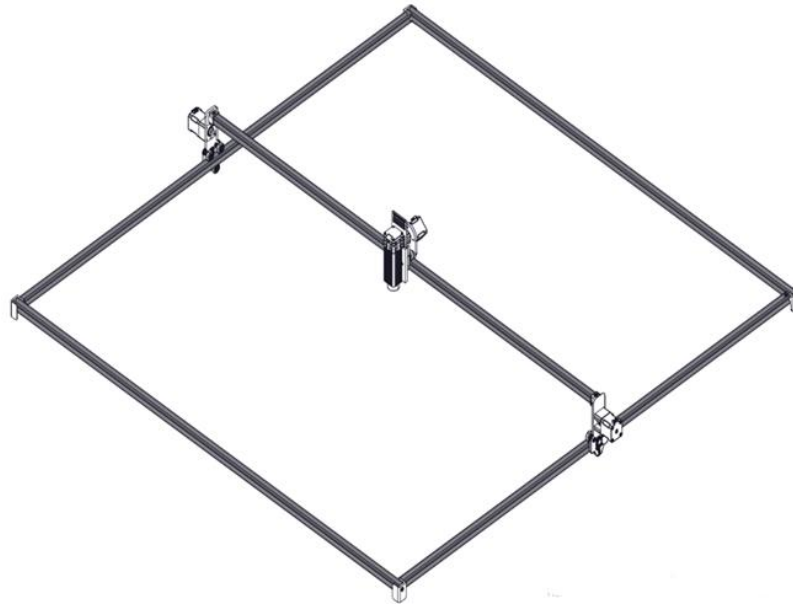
Загальний вигляд верстата для гравіювання
